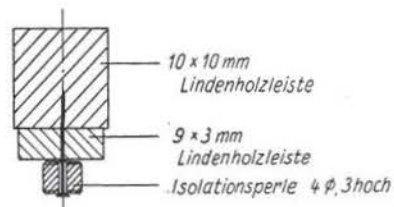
Aufbau eines Fahrzeuges der Rillenbahn
